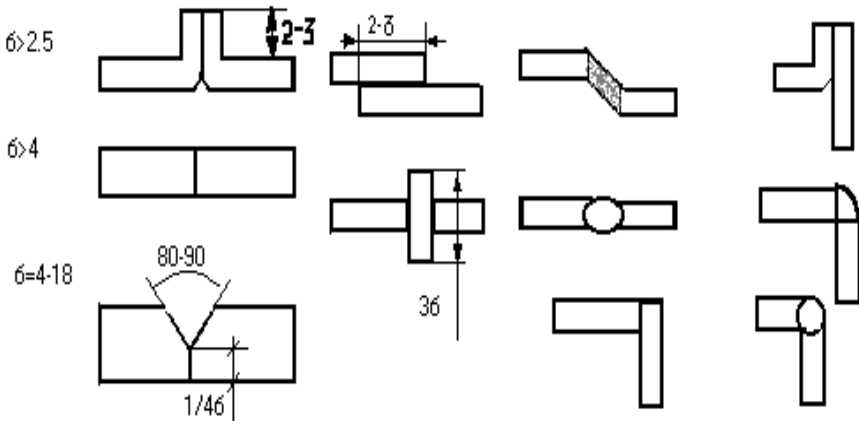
Схема підготовки крайок при зварюванні алюмінієвих з'єднань
